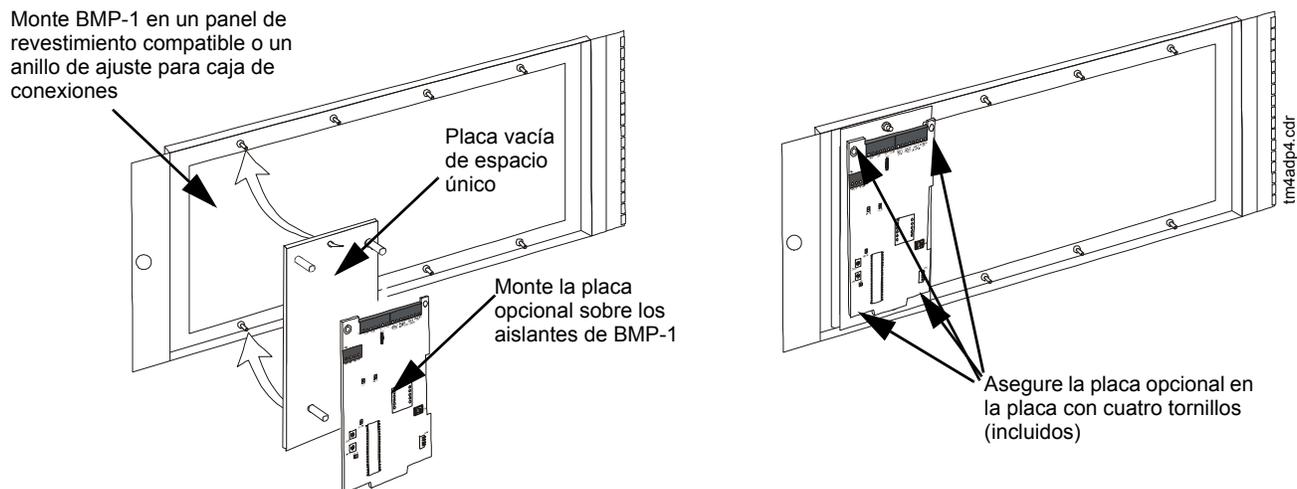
Montaje de una placa opcional sobre un panel de revestimiento con BMP-1 (Se muestra ADP-4B)
